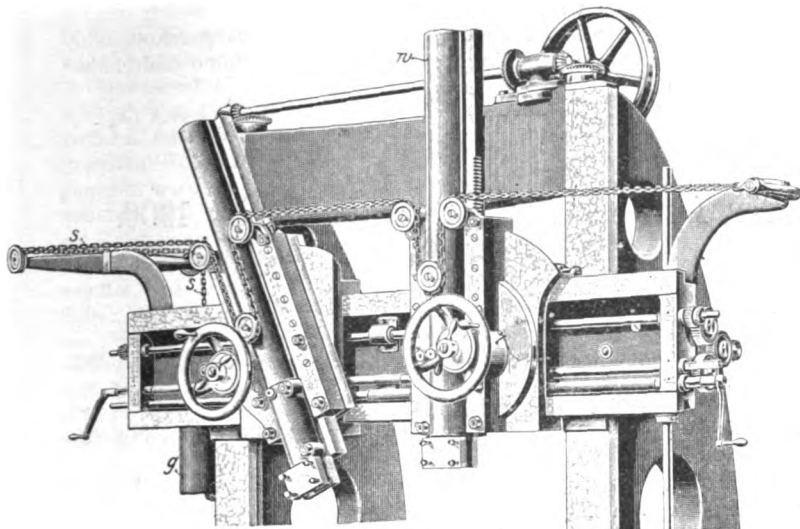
Aufhängung einer Senkrecht-Bohrspindel.
